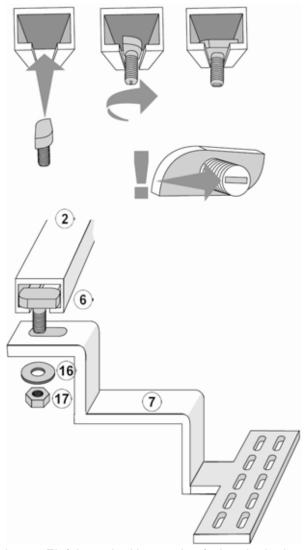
Einführen der Hammerkopfschraube in das C-Profil und bis zum Anschlag drehen. Durch die Kerbe am Gewindeende kann die korrekte Position der Schraube überprüft werden.
